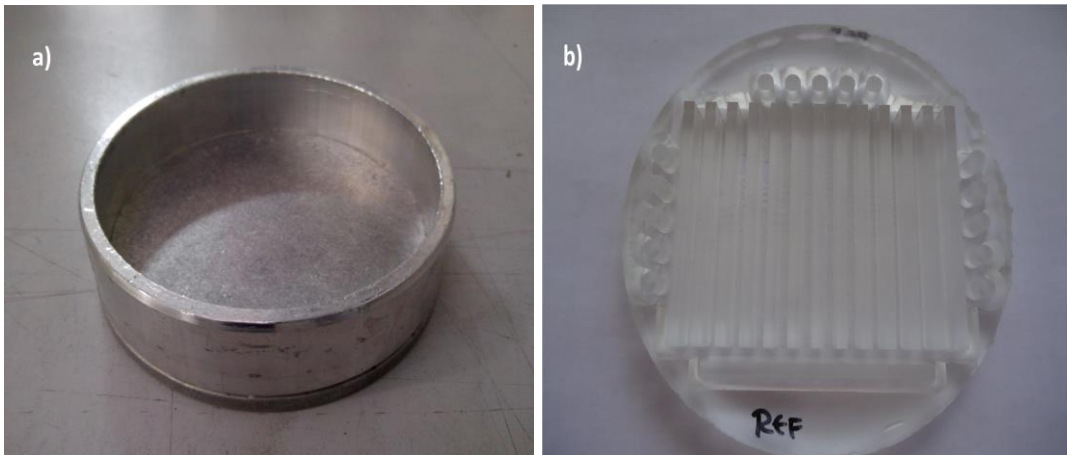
a) molde de alumínio utilizado para polimerização b) bloco polimerizado e com os corpos de prova após processo de usinagem.
